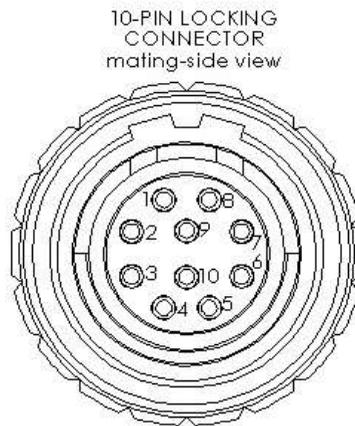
10poliger Stecker des CBL 203 oder CBL208 in direkter Draufsicht
